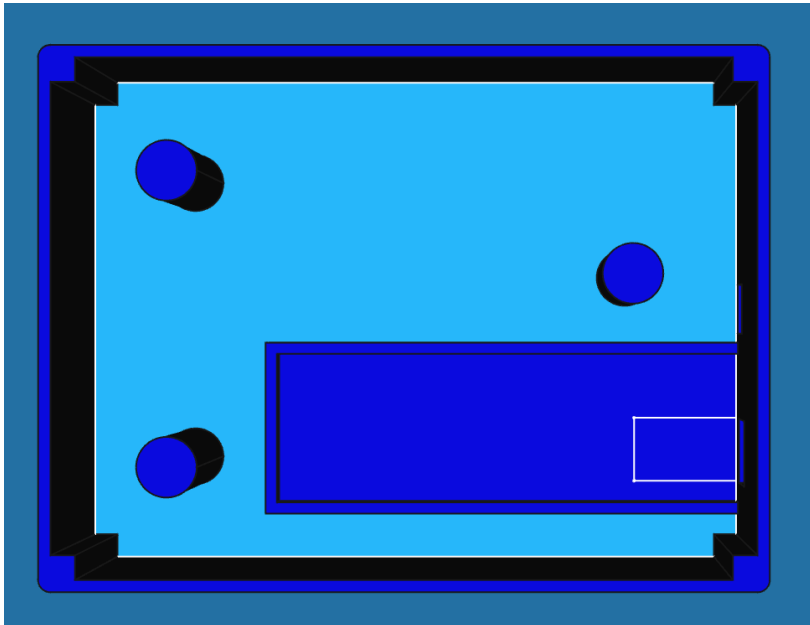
Gehäuse Unterteil mit Säulen für die Lochplatte und Aussparung für das Developmentboard
